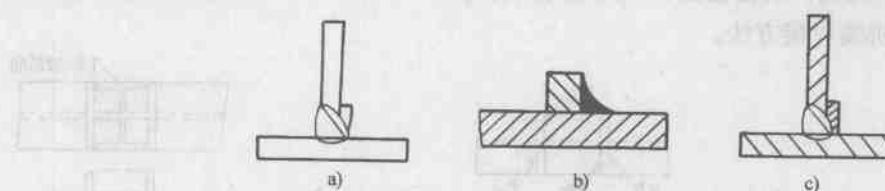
2 焊缝端面视图、剖视图和剖面图的表示方法
